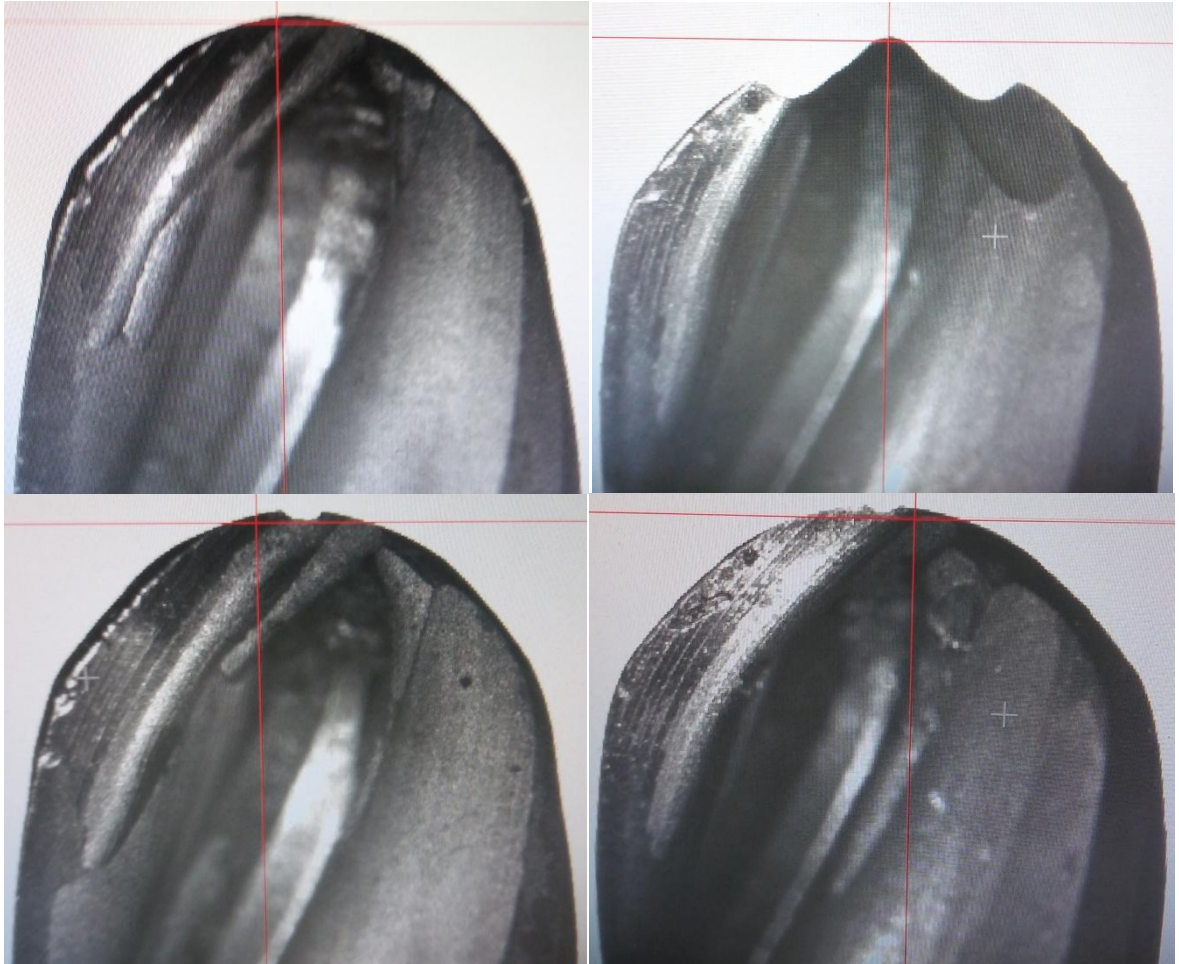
Режущая кромка фрезы без покрытия после обработки 1 лопатки
